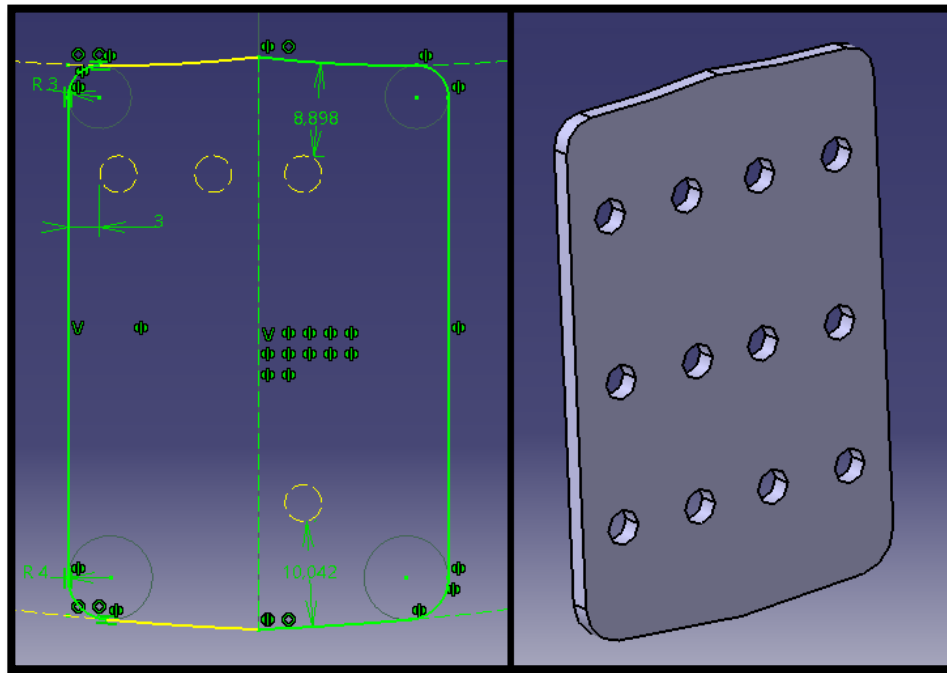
Refuerzo inferior 16: Sketch y pieza final tras extrusión y vaciado
